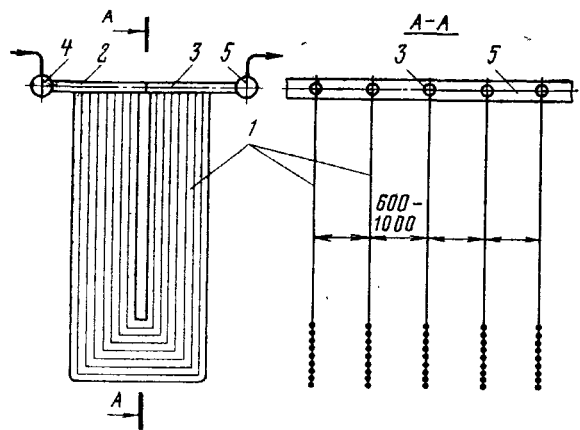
Вертикальный ширмовый пароперегреватель.
